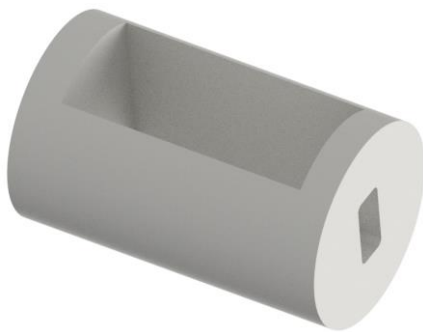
Mechanismus uzávěru tubusu šoupátkem
